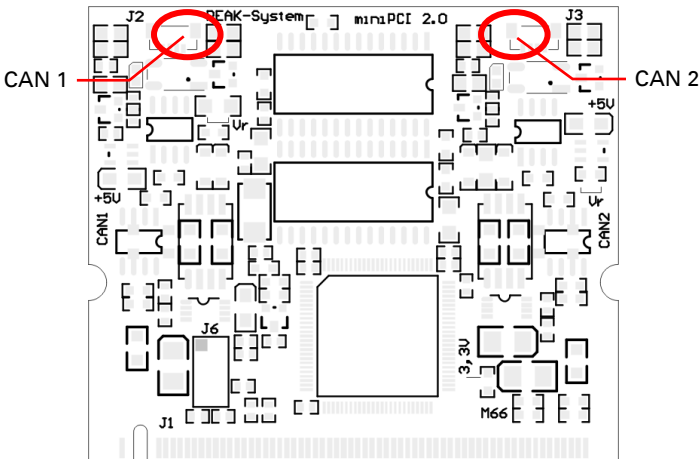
Positionen der CAN-Anschlüsse auf der PCAN-miniPCI-Karte
